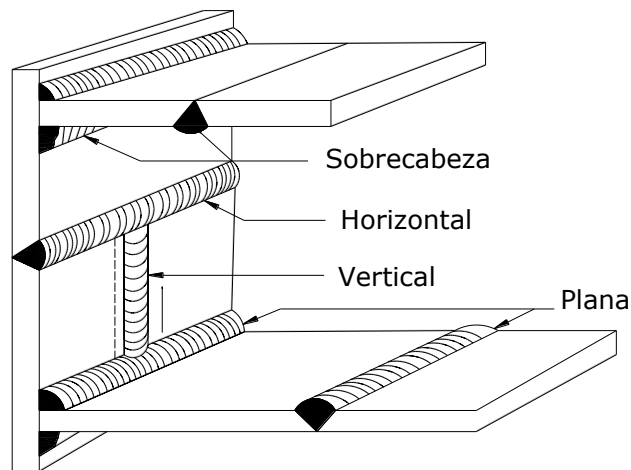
Ilustración del tipo de posición de soldadura.
